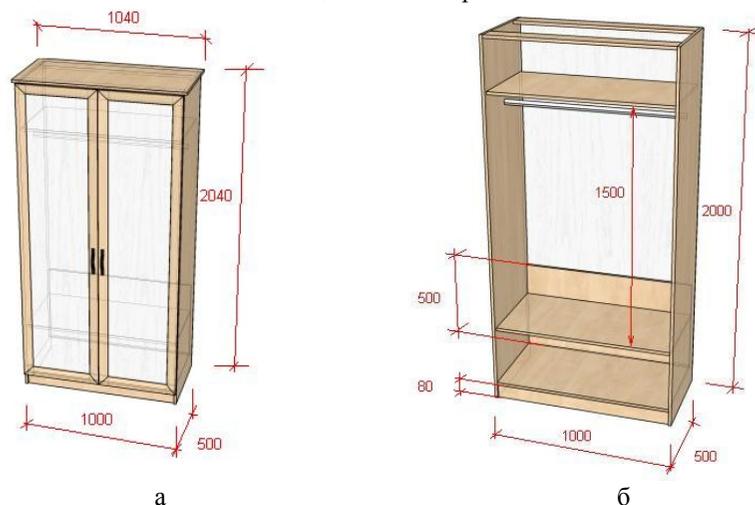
Шкаф для платья и белья: а – габаритные размеры; б – размеры короба
